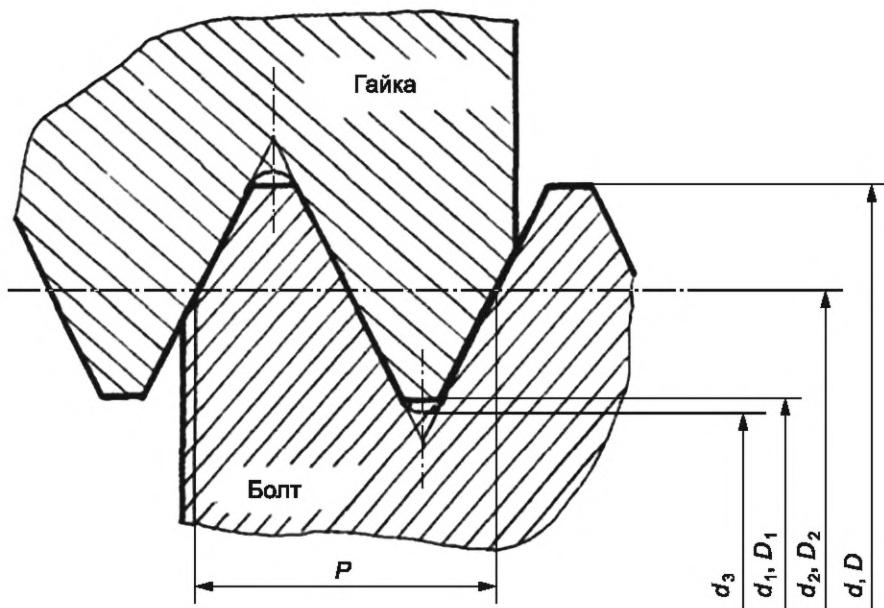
Профиль метрической резьбы с обозначением его элементов
